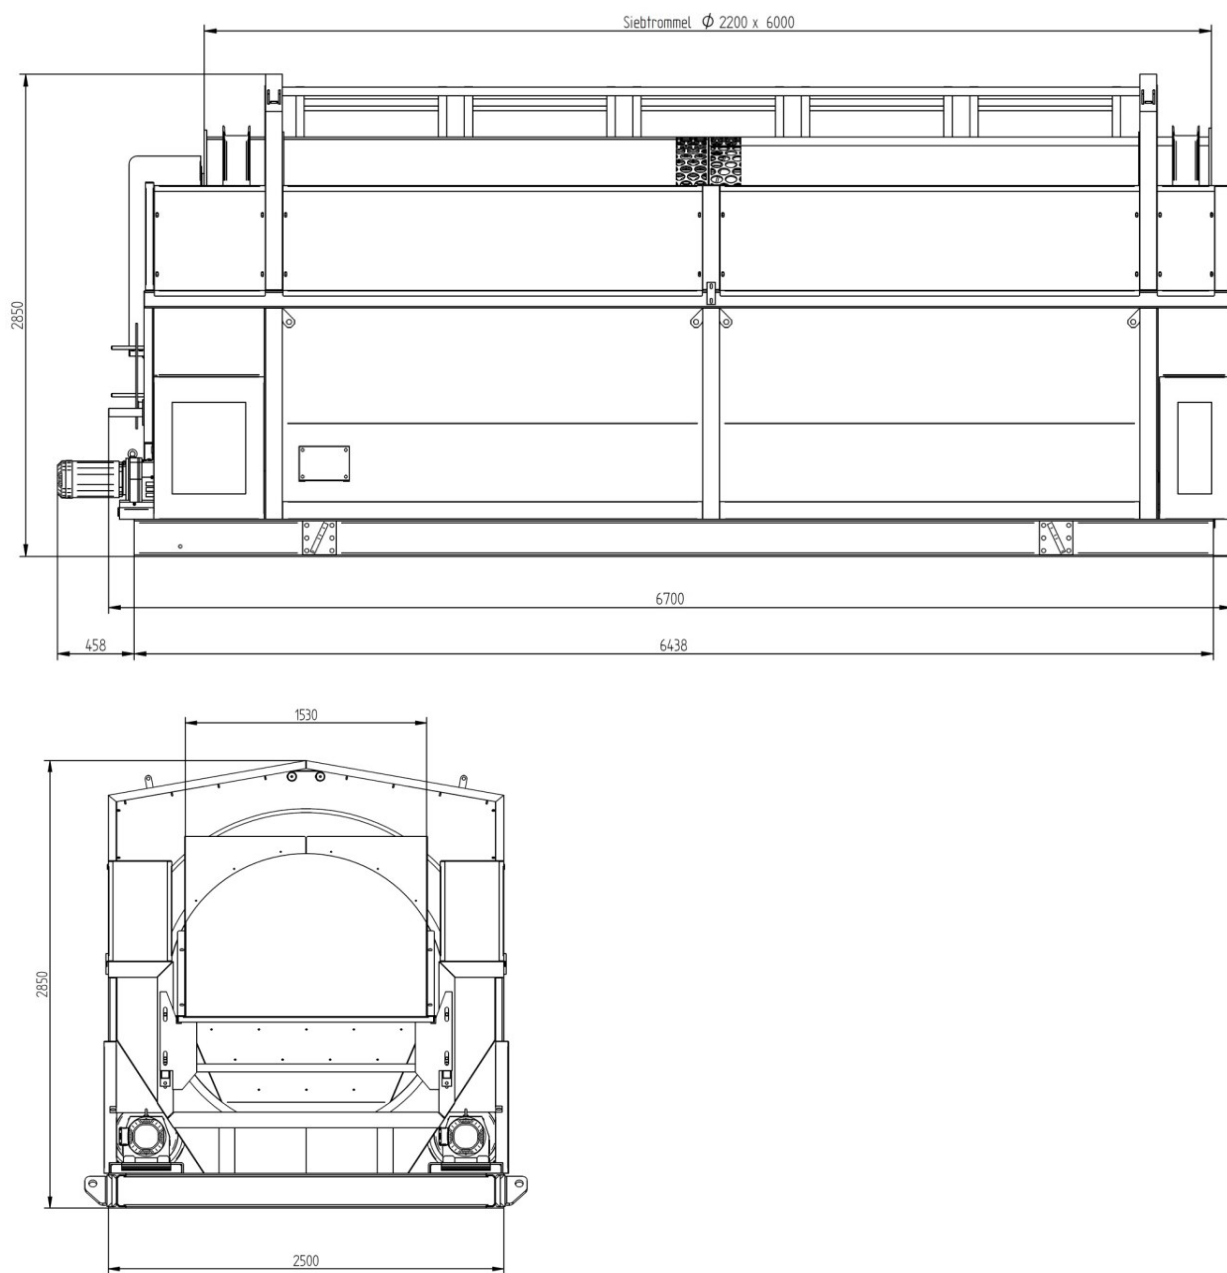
Габаритный чертеж барабанного грохота (транспорт)
